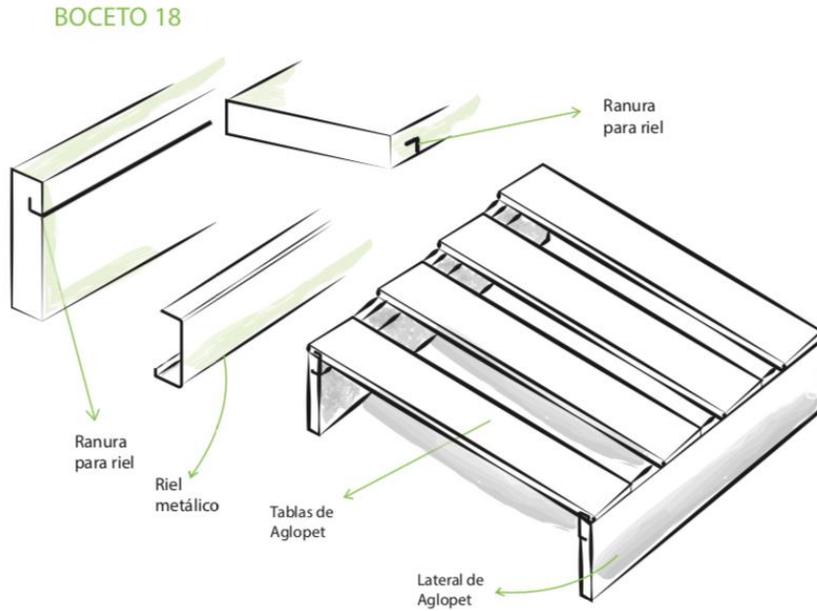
Dibujo técnico alternativa 17. Fuente: La Autora.
